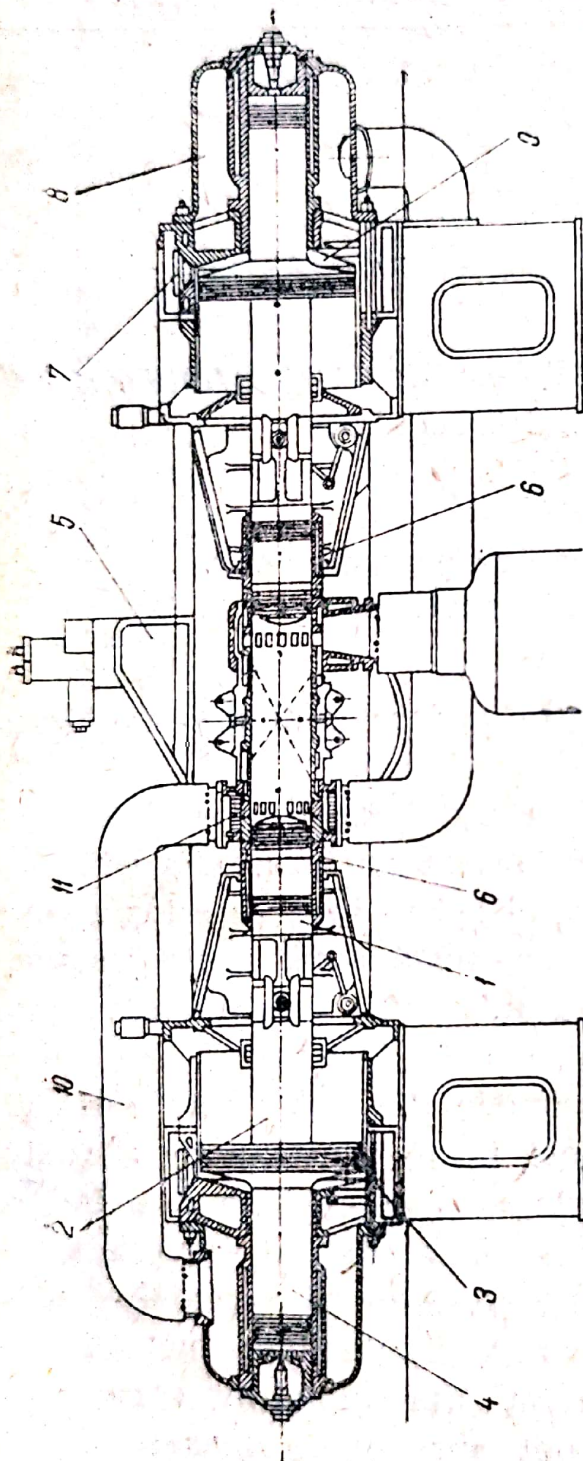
Generatorul de gaze cu pistoane libere de construcție sovietică.
